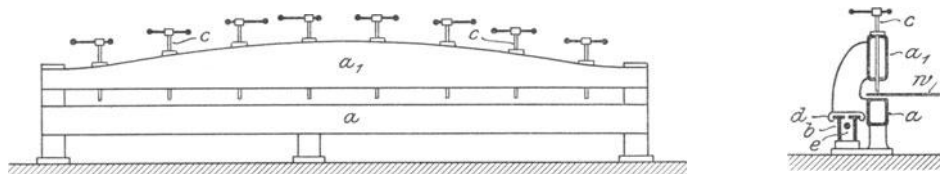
u. 13. Blechkantenhobelmaschine (1864).
